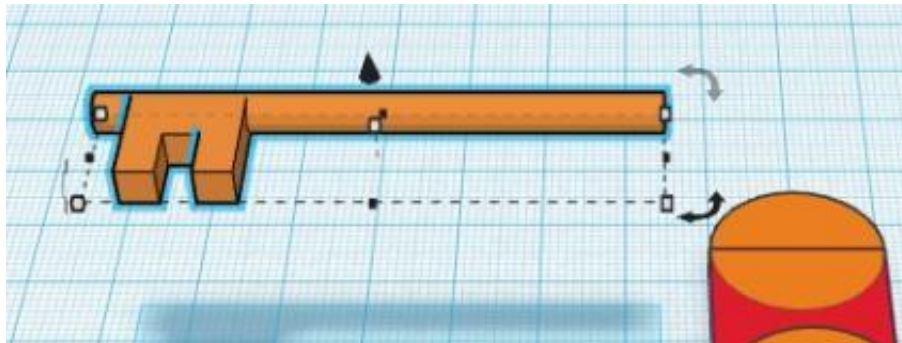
TIGE ET PANNETON PARALLÈLES AU PLAN DE CONSTRUCTION
